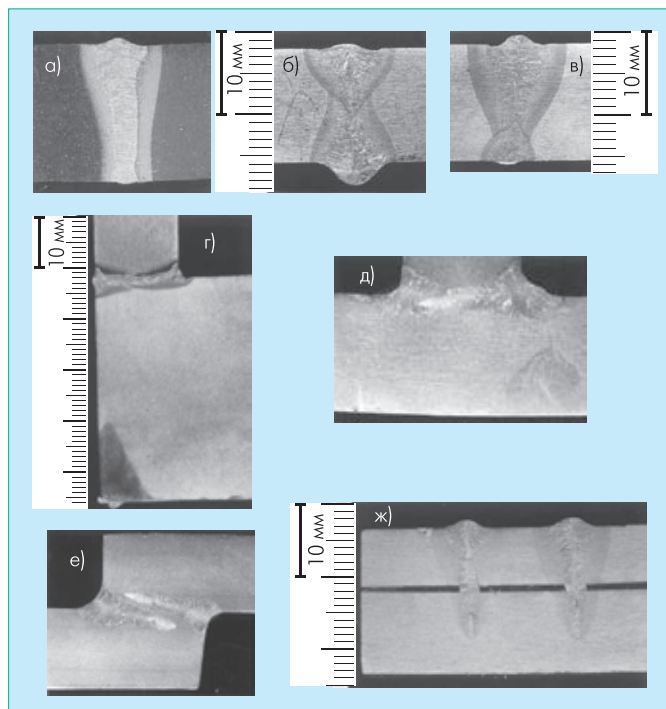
Макрошлифы сварных соединений: стыкового одно-стороннего (а), двухстороннего (б), с подваркой корня шва (в), углового (г), таврового (д), нахлесточного (е), проплавного 3-слойного (ж). Использовалась корпусная сталь 09Г2С (а), высокопрочная сталь 12ХН4МДА (б–г, ж), высоколегированной коррозионно-стойкой стали 08Х18Н10Т (д–ж). Сварка выполнялась на CO₂-лазере "Ижора-М" [11, 19]
